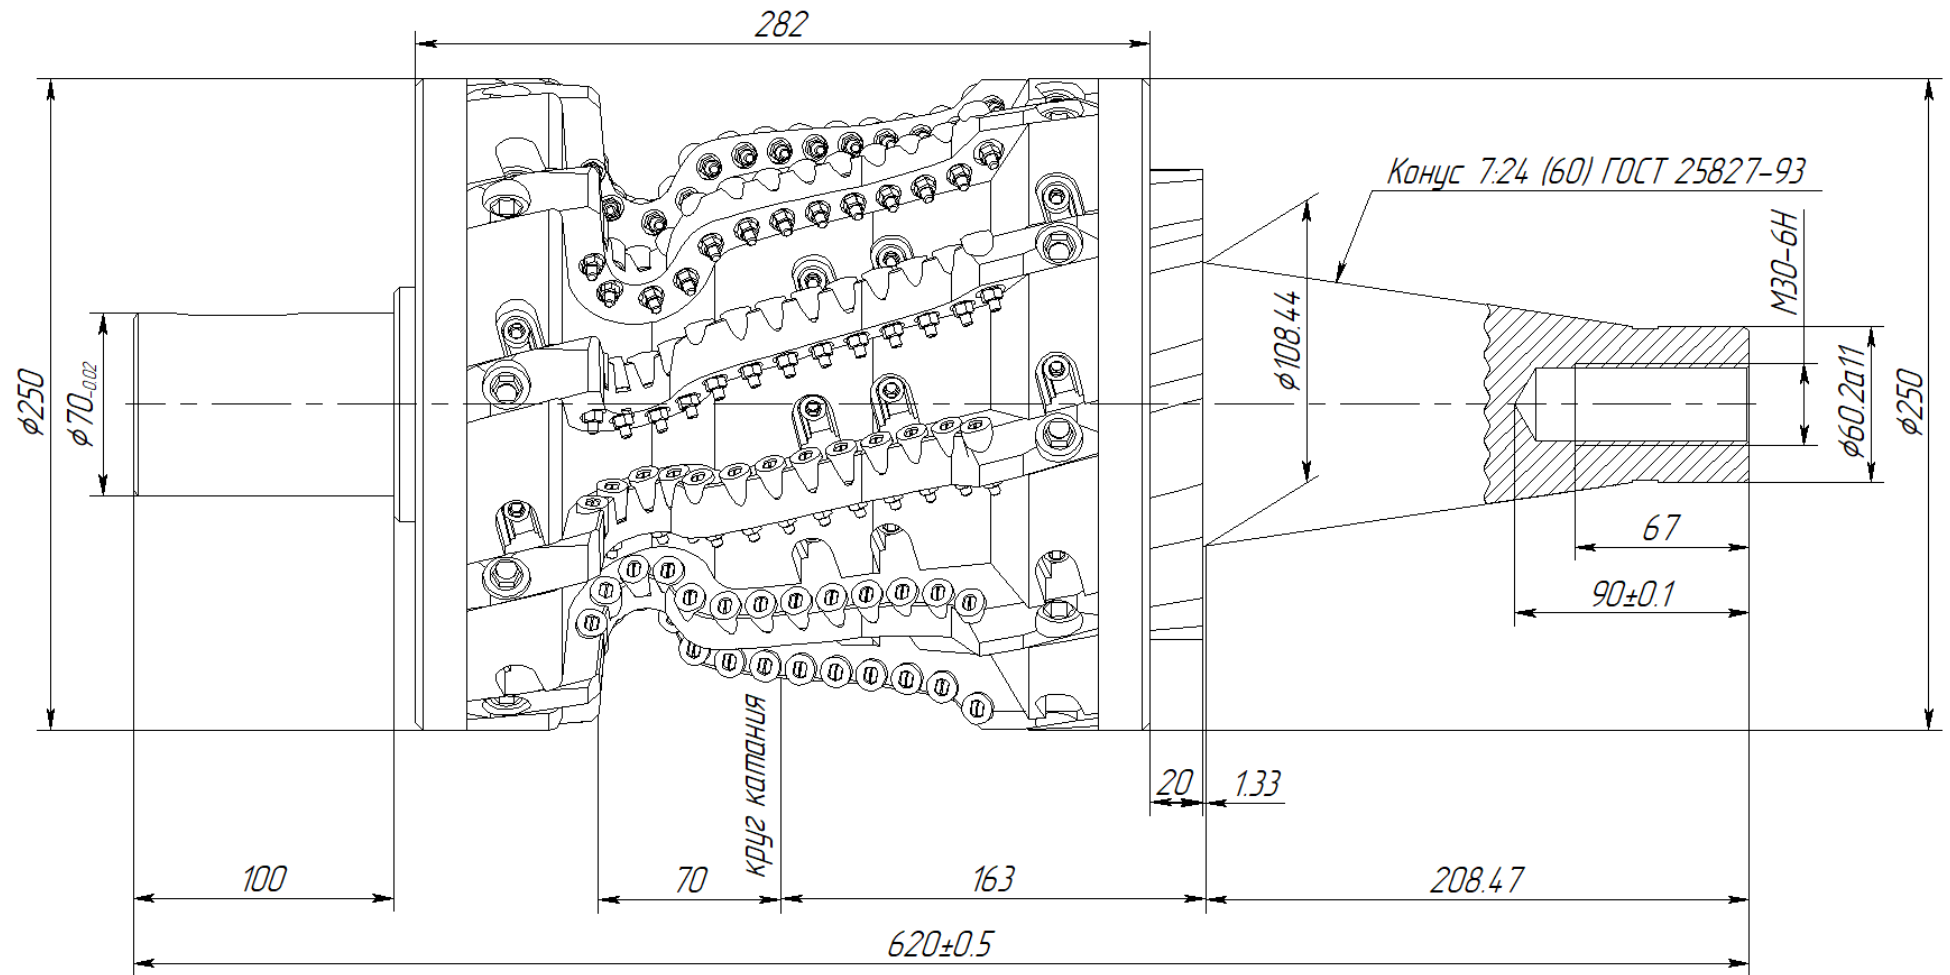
Рабочий чертеж сборной фасонной фрезы с СМП.
